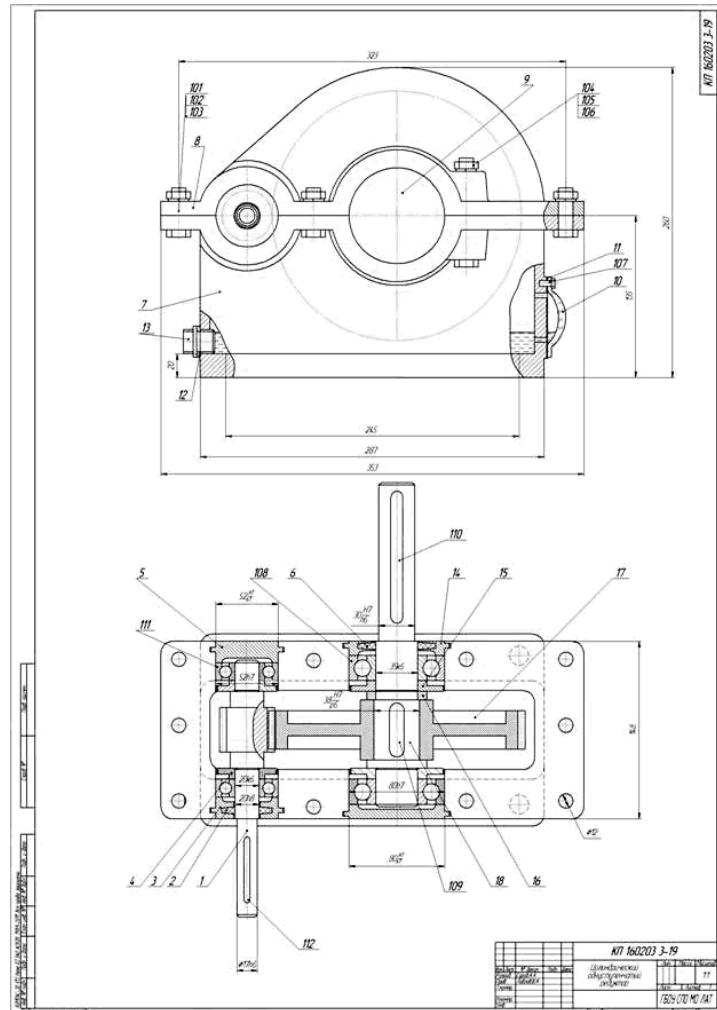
Чертеж цилиндрического одноступенчатого редуктора.
